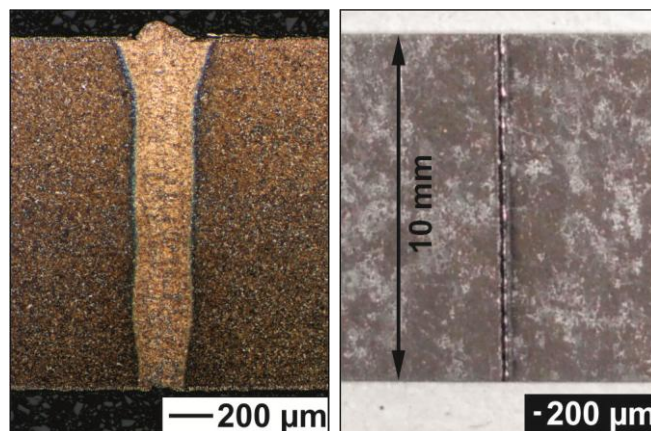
Typische Stumpfstoß-Laserschweißnähte; Links: Querschliff einer Schweißnaht (Schweißgeschwindigkeit: 20 m/min, Nahtbreite 250 µm), Rechts: Ansicht 10 mm Schweißnahtoberraupe
